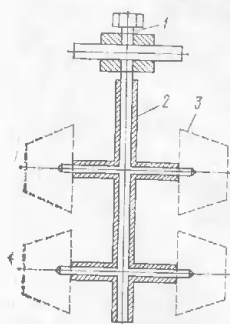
Подвесное приспособление с жестко закрепленными формами:
